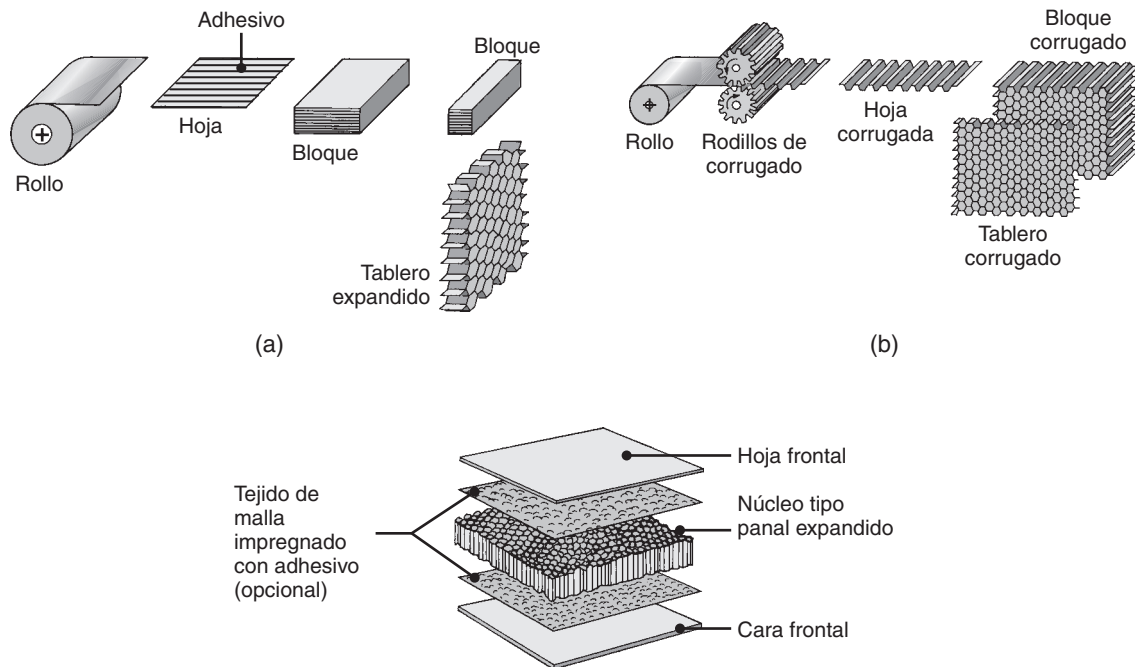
Métodos de manufactura de estructuras tipo panel: (a) proceso de expansión; (b) proceso de corrugado; (c) ensamble de una estructura tipo panel en un laminado.
